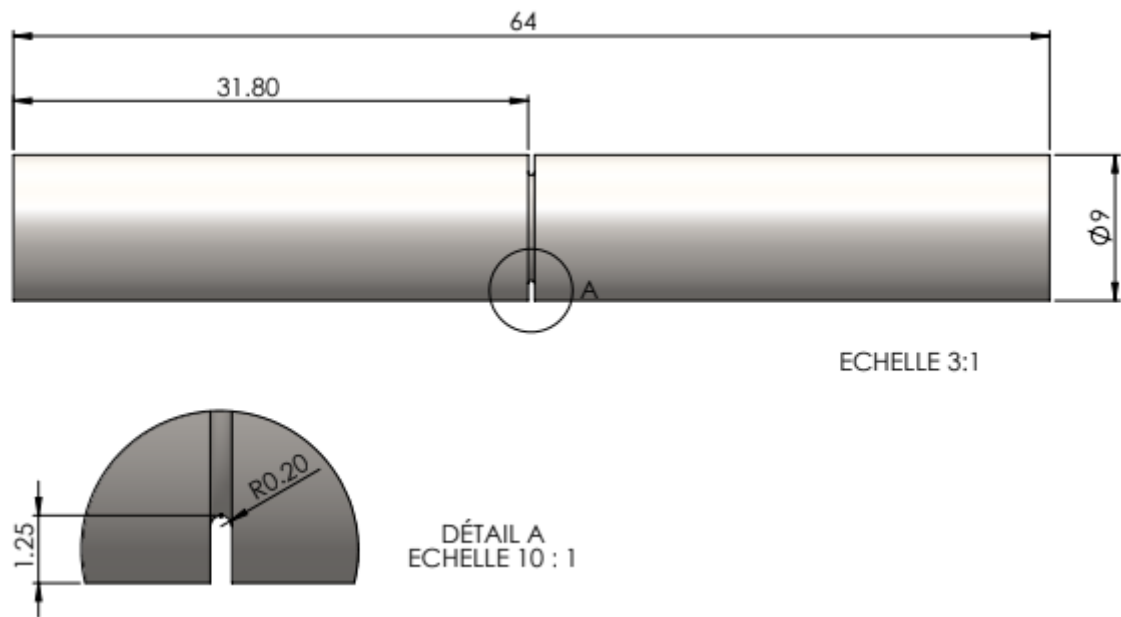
Géométrie et dimension de l'éprouvette U0.2.
